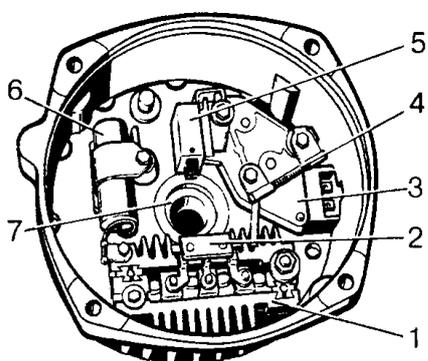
Внутренний вид задней крышки в сборе генератора IOSI - 100: 1 - выпрямительный блок; 2 - дополнительный выпрямитель обмотки возбуждения; 3 - регулятор напряжения; 4 - резистор 40 Ом; 5- щеткодержатель; 6 - помехоподавительный конденсатор; 7 - игольчатый подшипник
